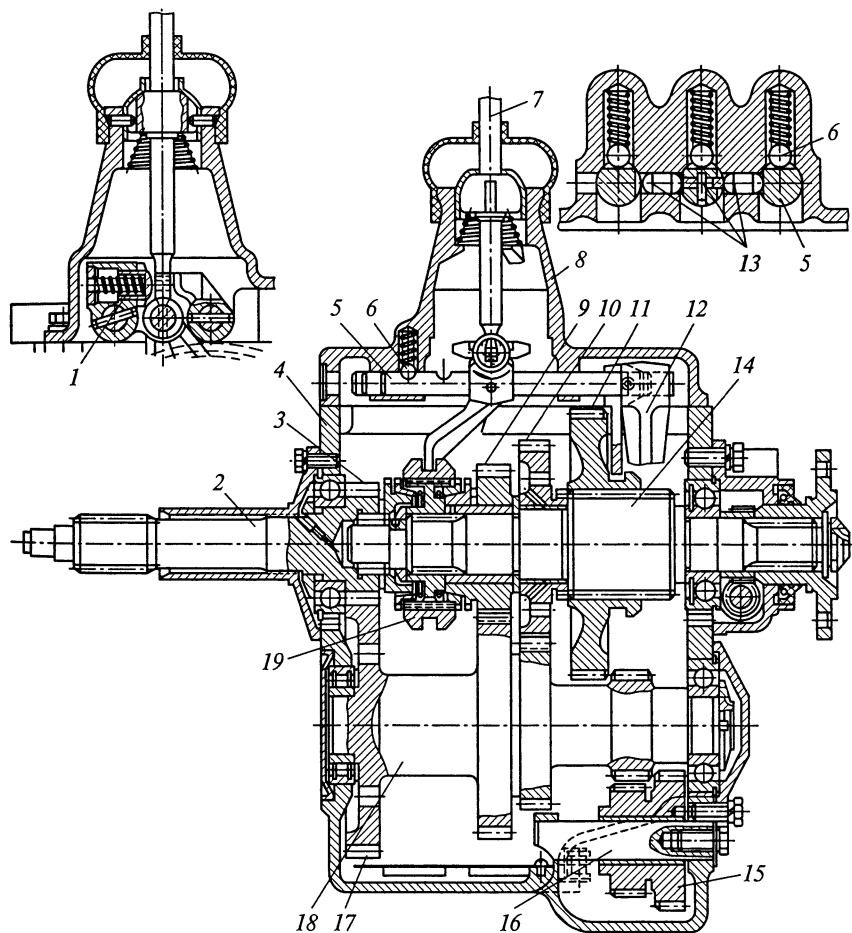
Коробка передач грузовых автомобилей ГАЗ:
